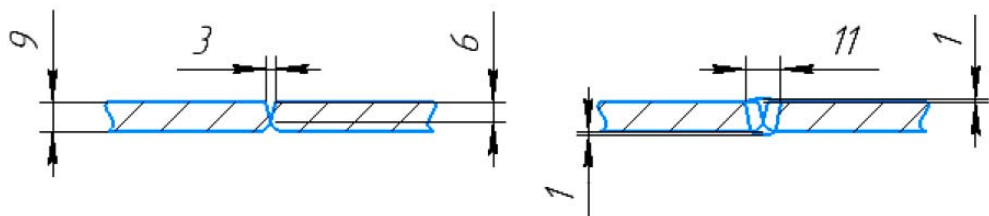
Геометричні розміри підготовки кромки для зварювальних швів
